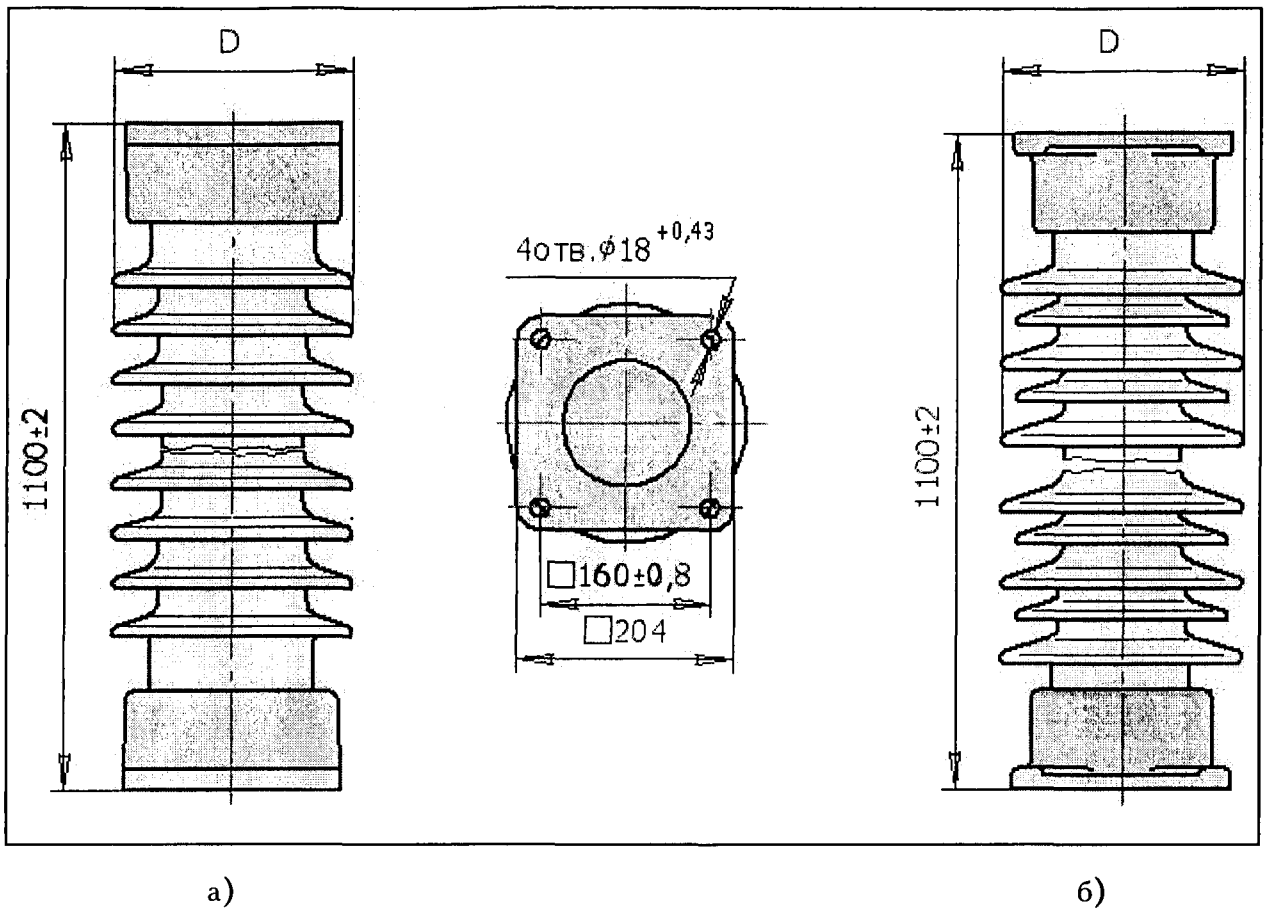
Габаритные размеры опорных стержневых изоляторов типа ИОС-110-600 УХЛ1
